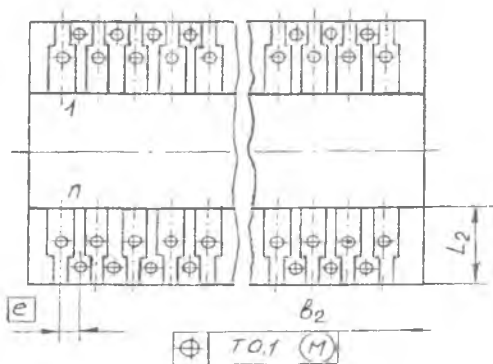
Конструкция корпуса типа 5 подтипа 2
